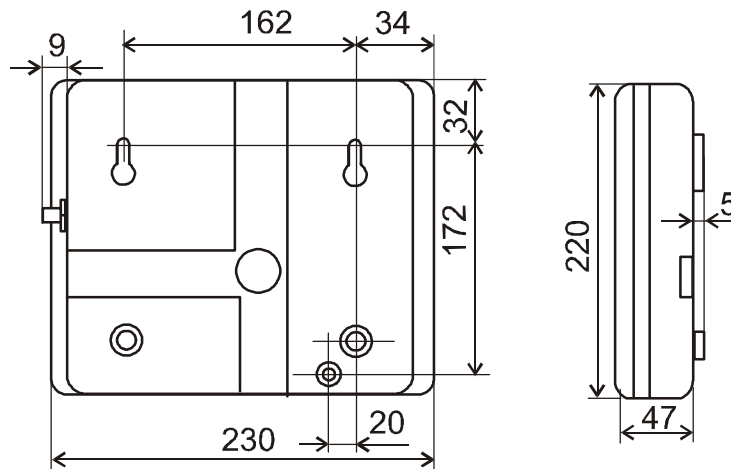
Внешний вид прибора, установочные и габаритные размеры
